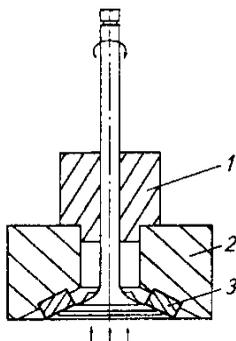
Схема обработки фаски клапана резцовой головкой:
